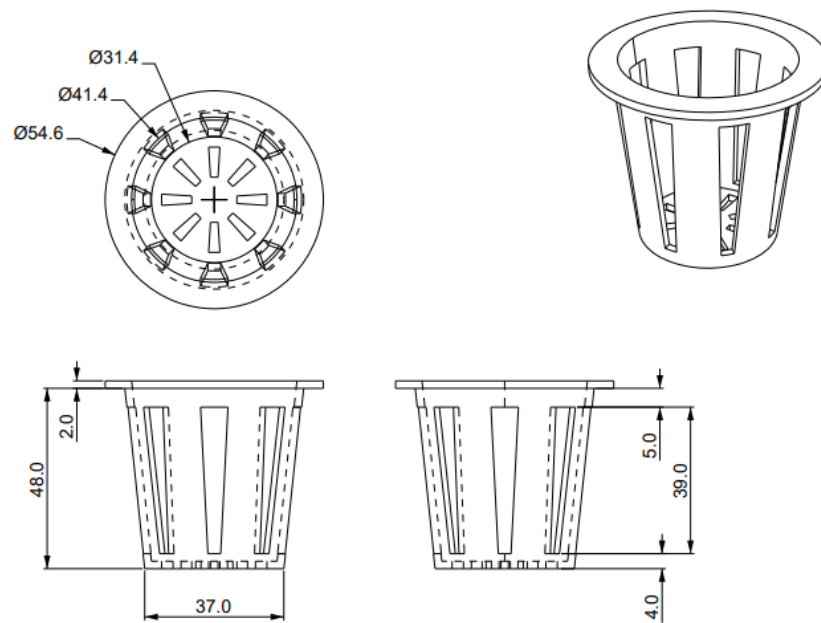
Plano de la cesta de plantación que componen el dispositivo.
